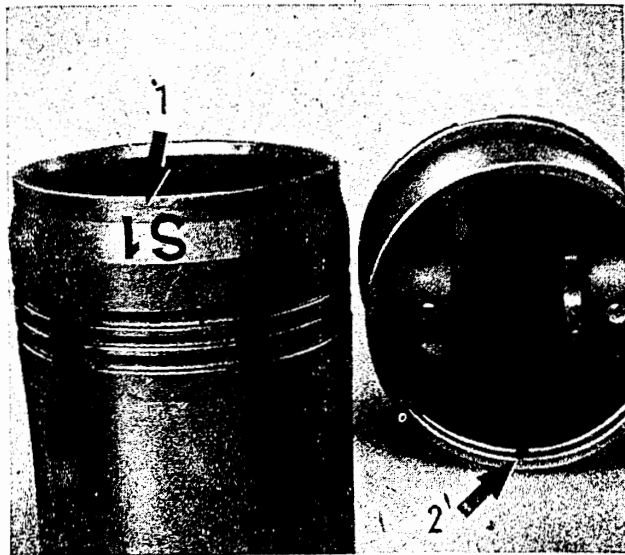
Verschleißstufenkennzeichnung auf Zylinderlaufbuchse (1) und Kolben (2)
